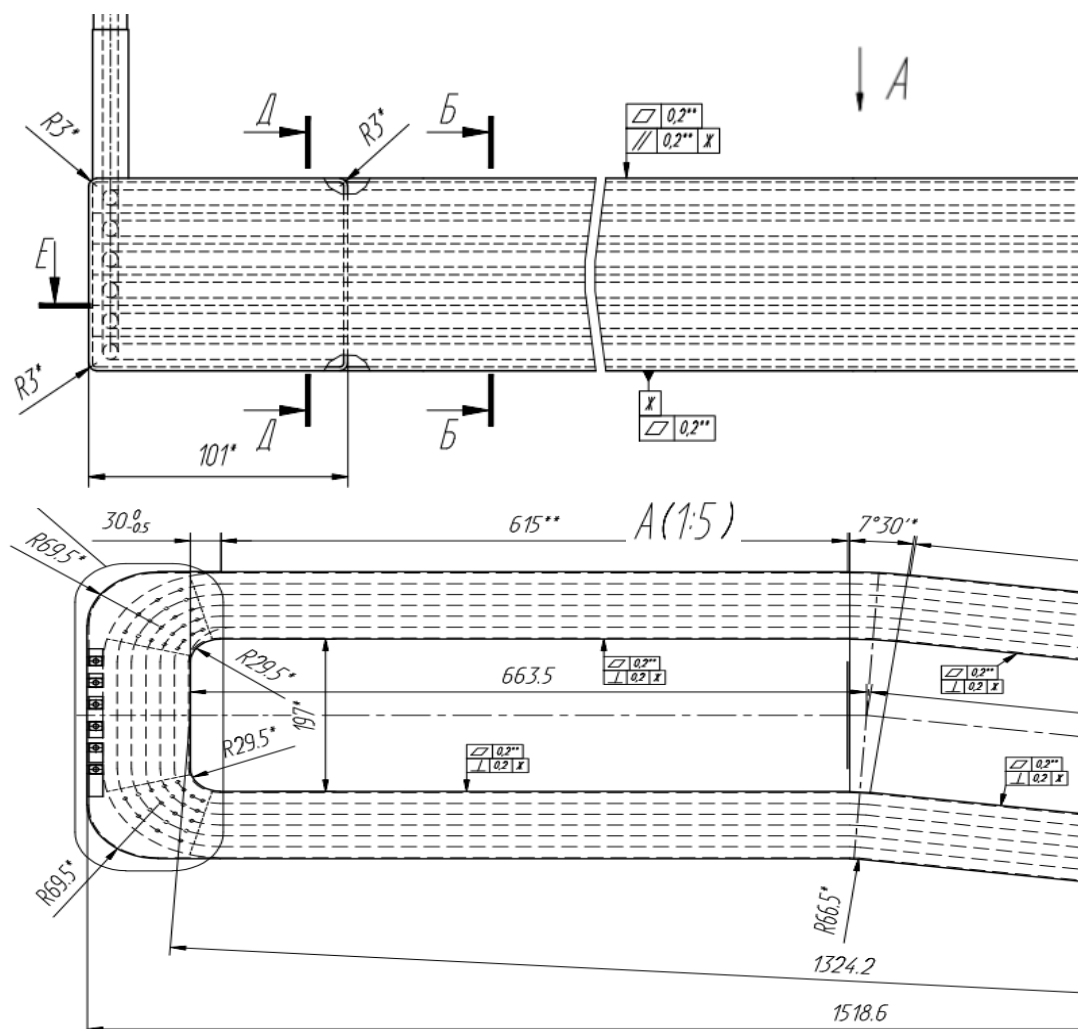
Фрагмент чертежа обмотки 9582-02-01-00 СБ магнита дипольного.
